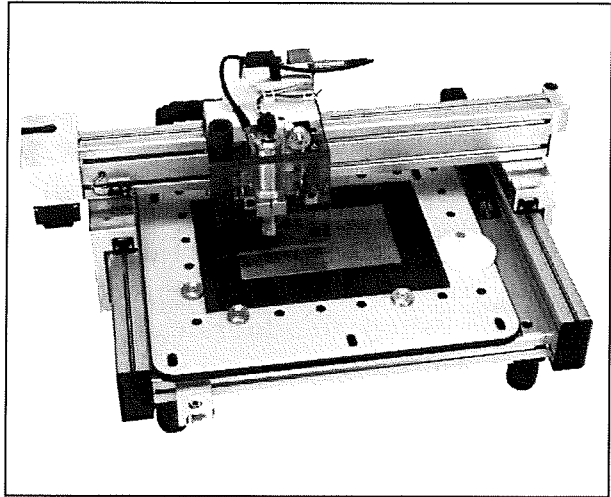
/8.3.19-9: De TechnoRoute machine van TechnoPrint-SMT.
